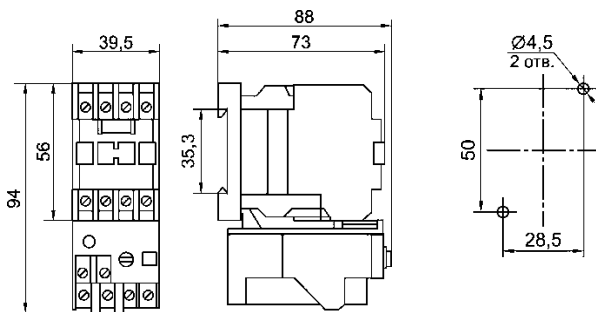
Пускатель неререверсивный ПМ12-010 10А. Степень защиты - IP00; IP20.
